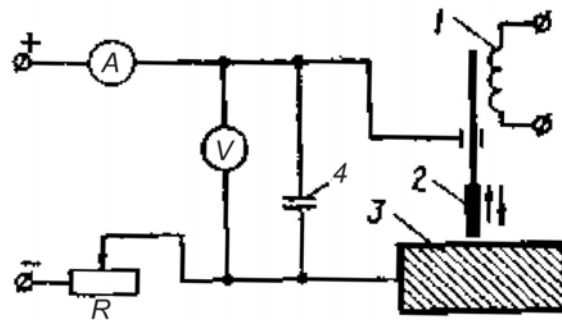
Принципова схема установки для електроіскрового нарощування деталей:
